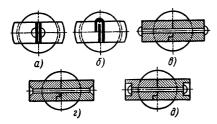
Конструкции сепараторов: a — змейковый; δ — с отогнутыми усиками; ϵ — массивный клепаный; ϵ и δ — массивные с потайными головками
